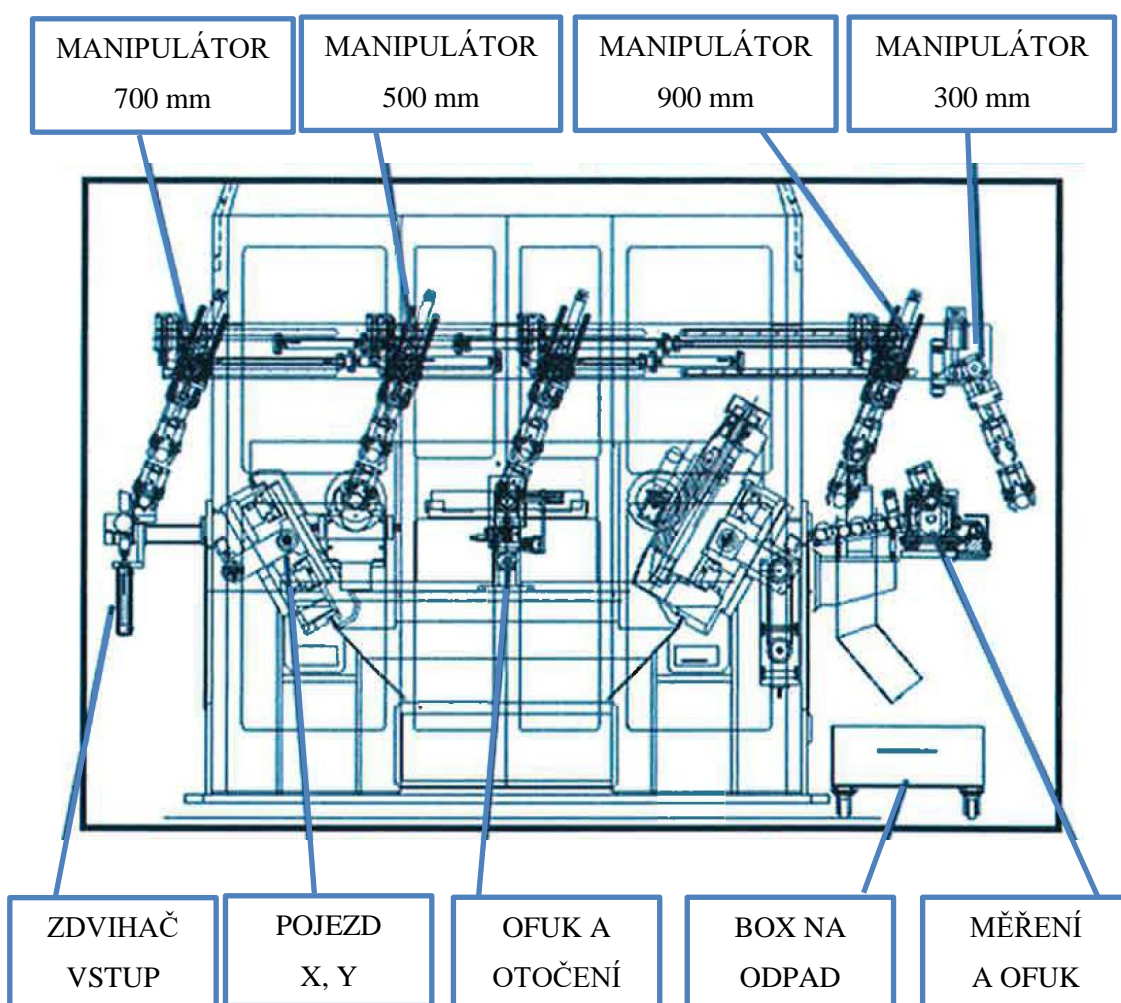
Dvojitý CNC obráběcí soustruh [63]
